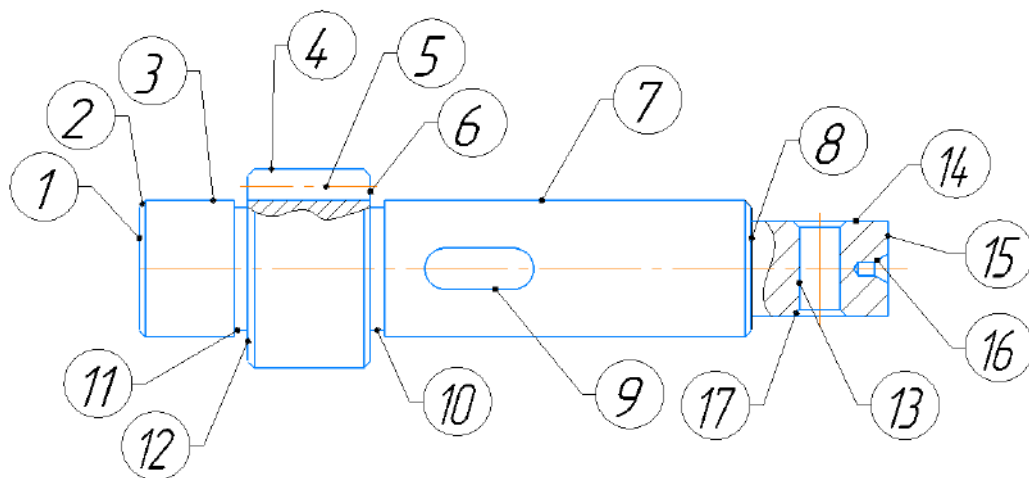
Технологічна розмітка поверхонь вала-шестерні
